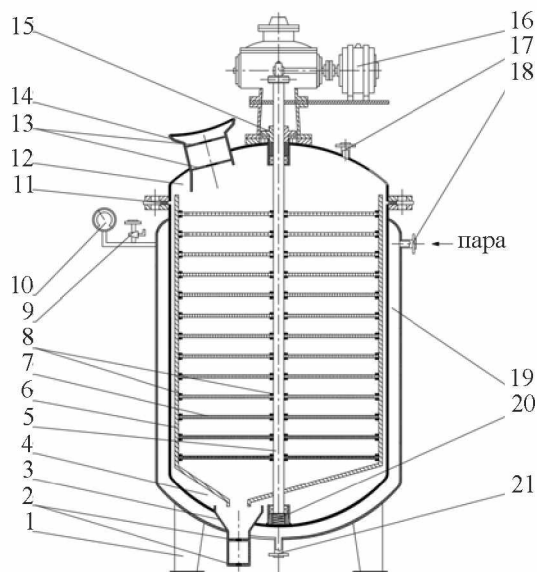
Вібраційна вакуумна сушарка безперервної дії для сушіння овочевої сировини: 1 — опори; 2 — запірний клапан; 3 — горловина; 4 — робоча камера; 5 — робочий вал; 6 — каркас для лотків; 7 — лотки з отворами змінного перетину; 8 — суцільне зварне з'єднання; 9 — клапан для видалення надлишкового тиску; 10 — манометр; 11 — затискач; 12 — кришка апарату; 13 — дозуючий клапан; 14 — завантажувальний бункер; 15 — ущільнювач; 16 — вібратор; 17 — трубопровід системи вакуумування; 18 — патрубок для подачі теплоносія; 19 — парова оболонка; 20 — патрубок для відведення конденсату; 21 — амортизаційна пружина
